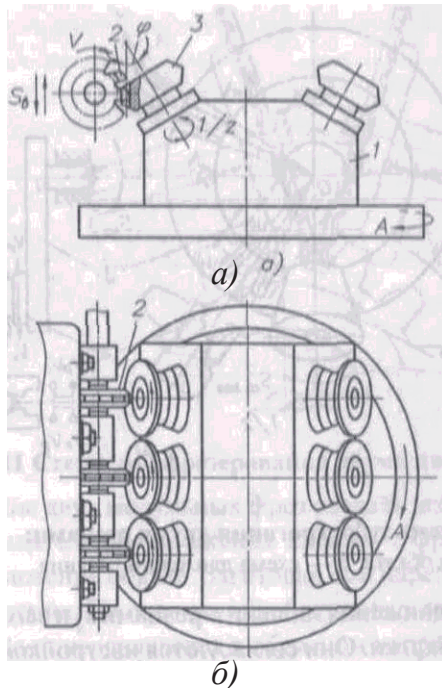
Многоместное поворотное приспособление для фрезерования конических колес: 1 – приспособления; 2 – модульная фреза; 3 – нарезаемое колесо
